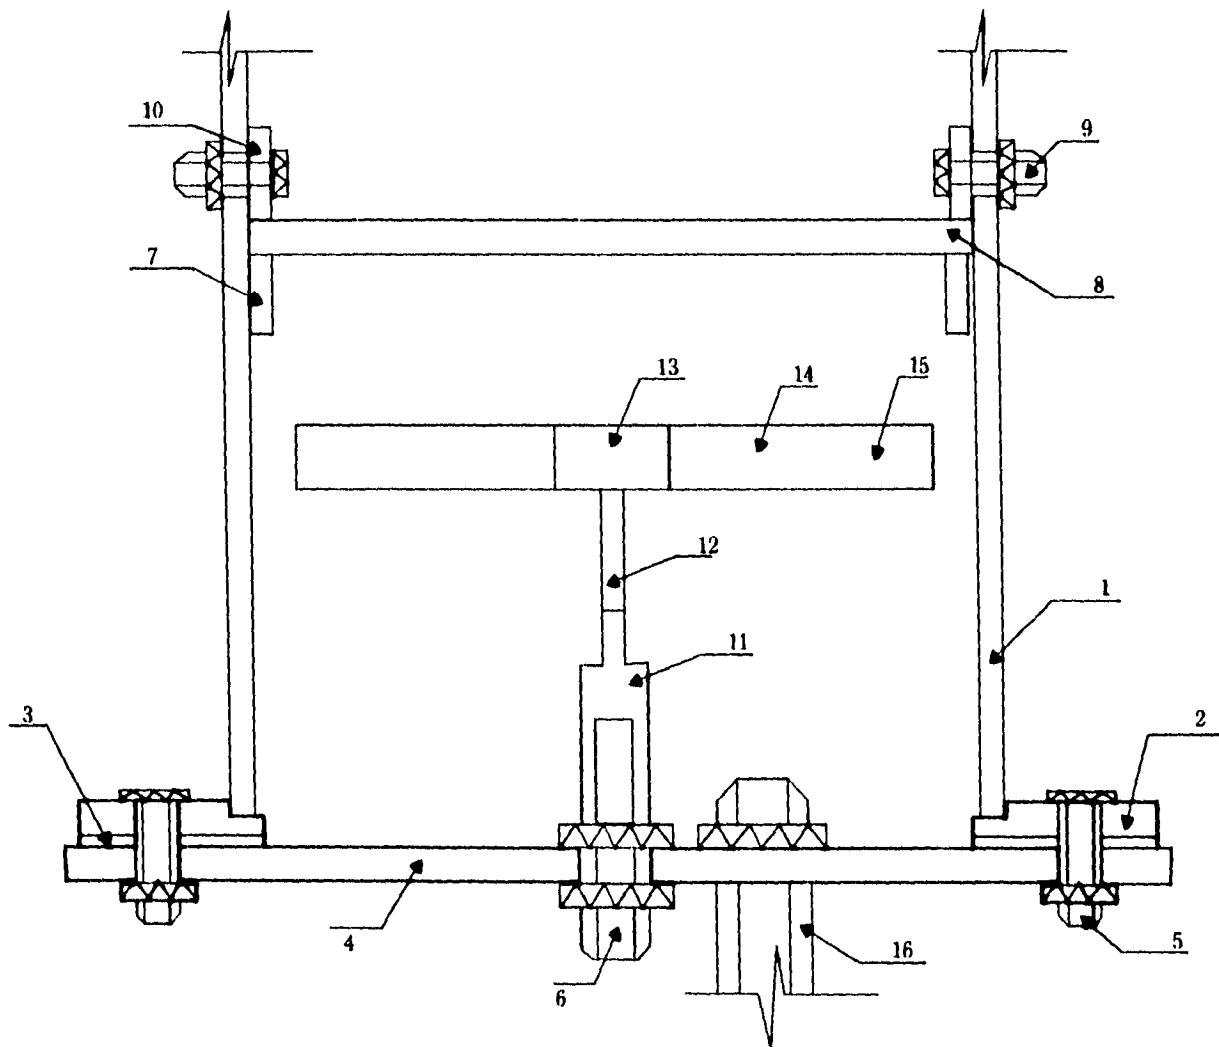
DETALLES DEL FALSO FONDO DE LA COLUMNA DE FILTRACIÓN
